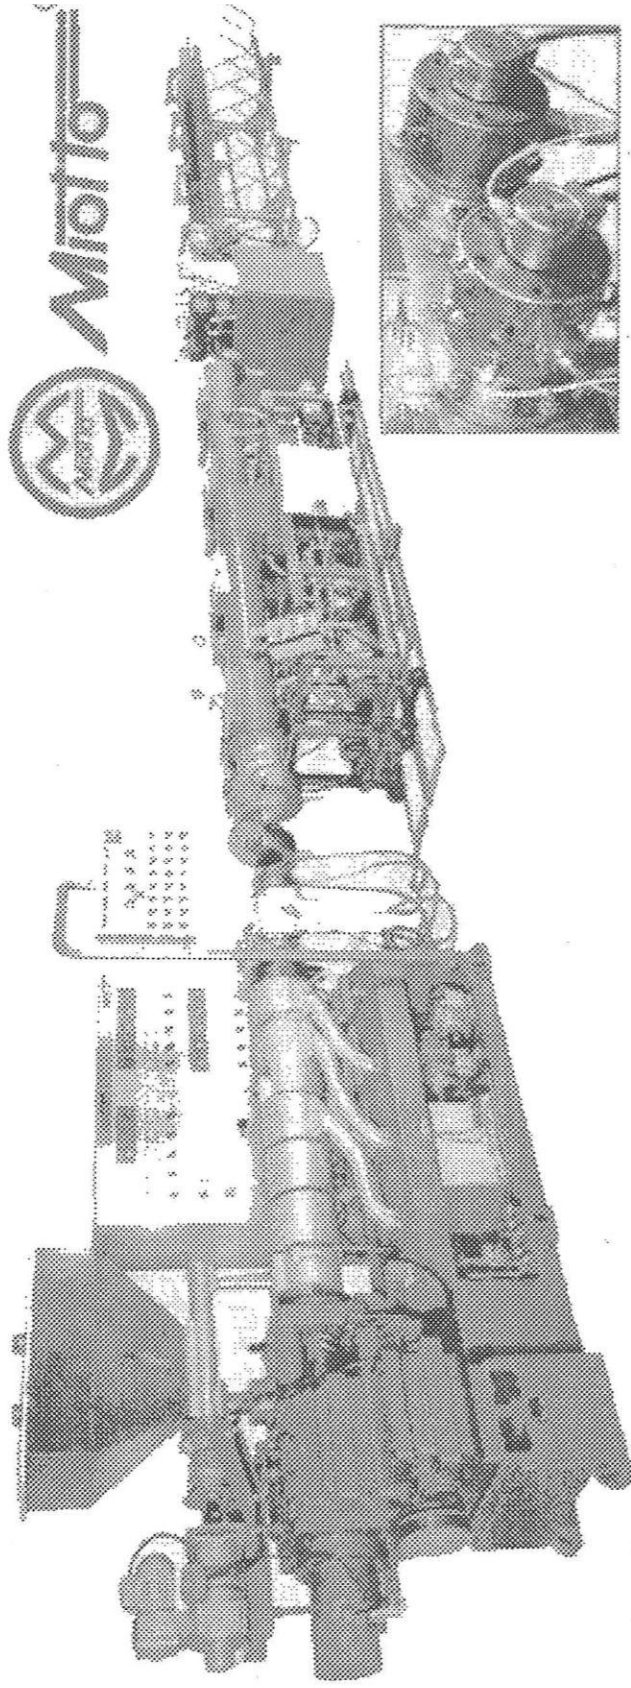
MÁQUINA DE MOLDEO POR EXTRUSIÓN
